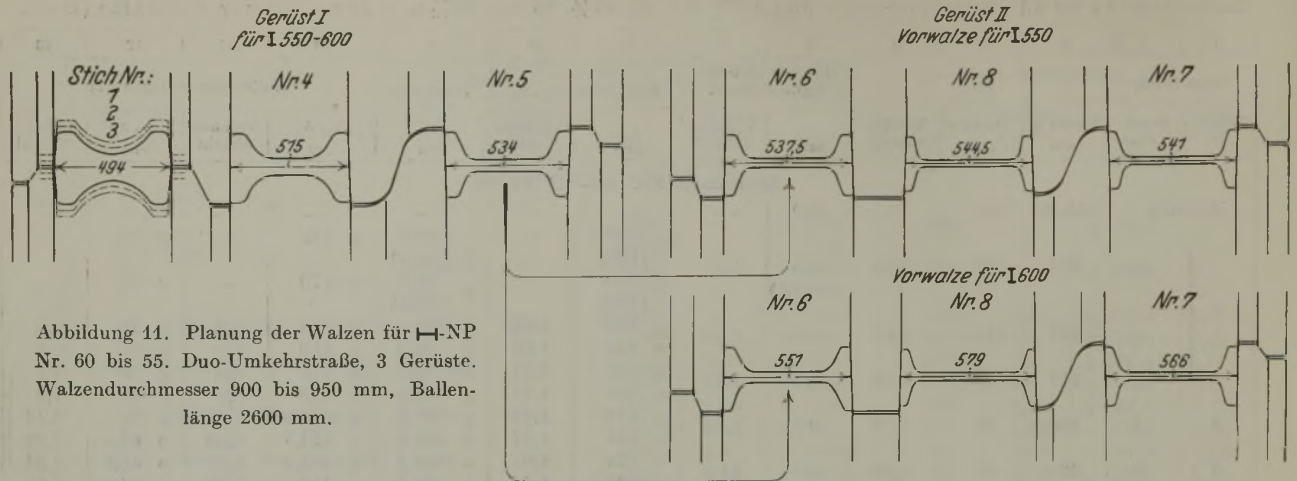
Planung der Walzen für I-NP Nr. 60 bis 55. Duo-Umkehrstraße, 3 Gerüste. Walzendurchmesser 900 bis 950 mm, Ballenlänge 2600 mm.
